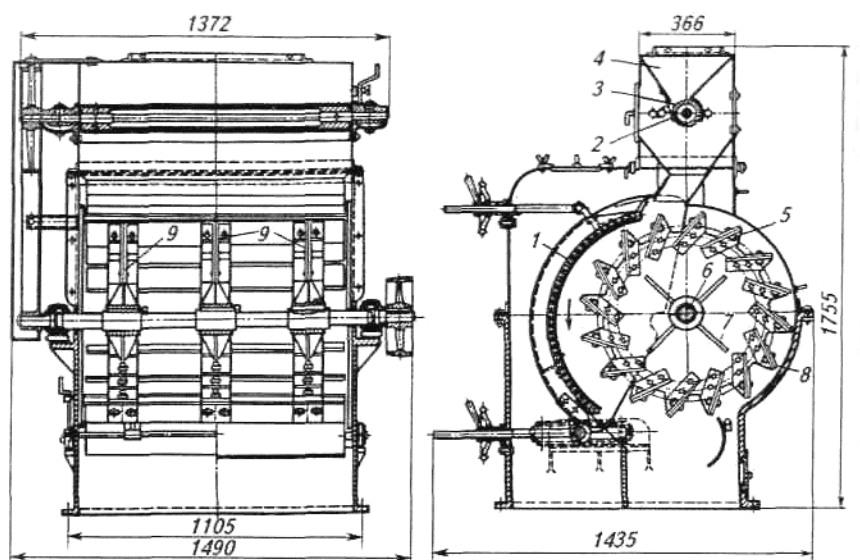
Бичевая обрушивающая машина типа МНР: 1 — дека; 2 — регулируемая заслонка; 3 — рифленый валик; 4 — питающий бункер; 5 — стойки бичей; 6 — уголок; 7 — ребра дисков; 8 — бичи; 9 — диски
